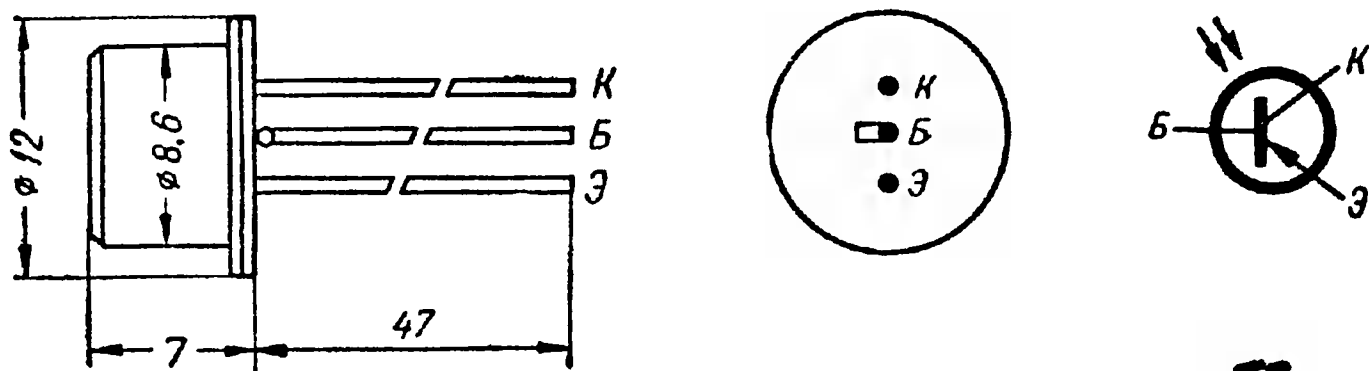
Основные размеры и схематическое изображение фотодиода ФТ-1.
